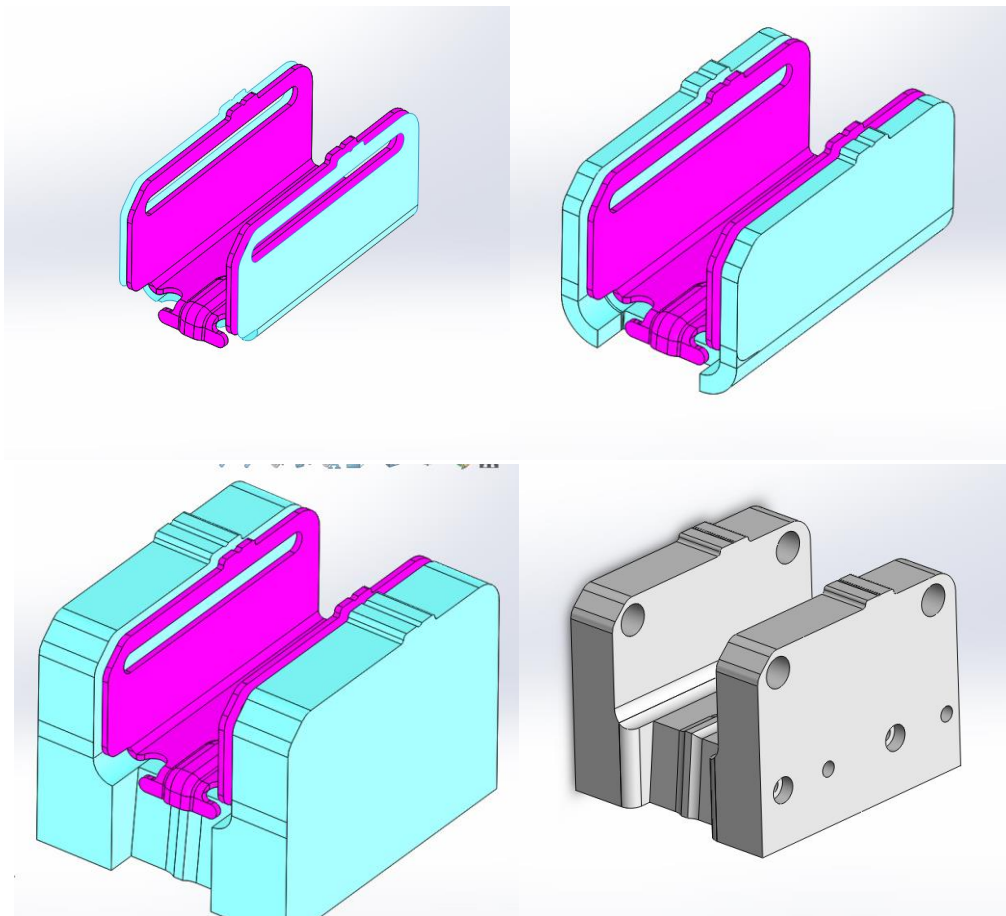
Modelado de bloque principal para dispositivo de medición
